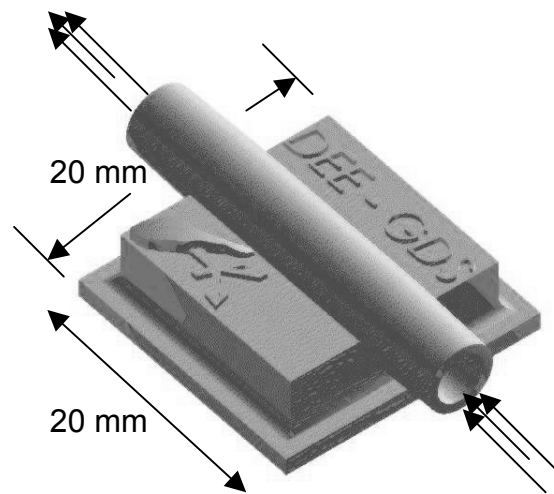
Dibujo CAD de la cápsula para el sellado de la estructura encapsulada en placa PCB
